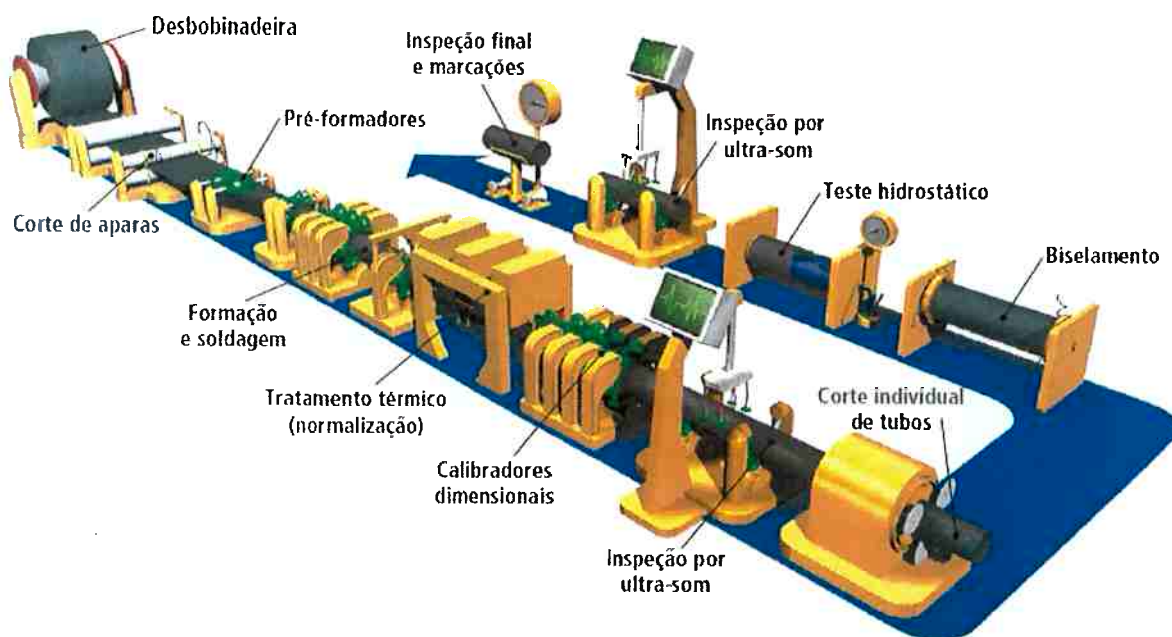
Fabricação dos tubos por formação contínua e soldagem ERW [16].
